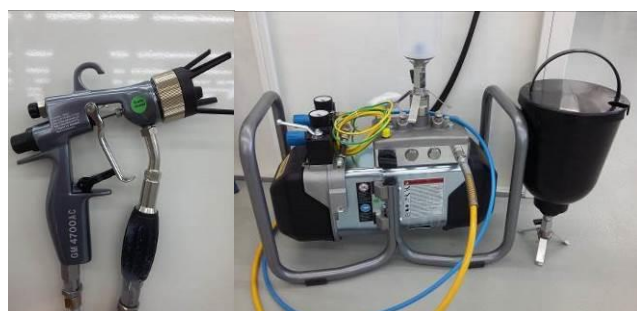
pistolet et pompe Wagner (photo FCBA)
